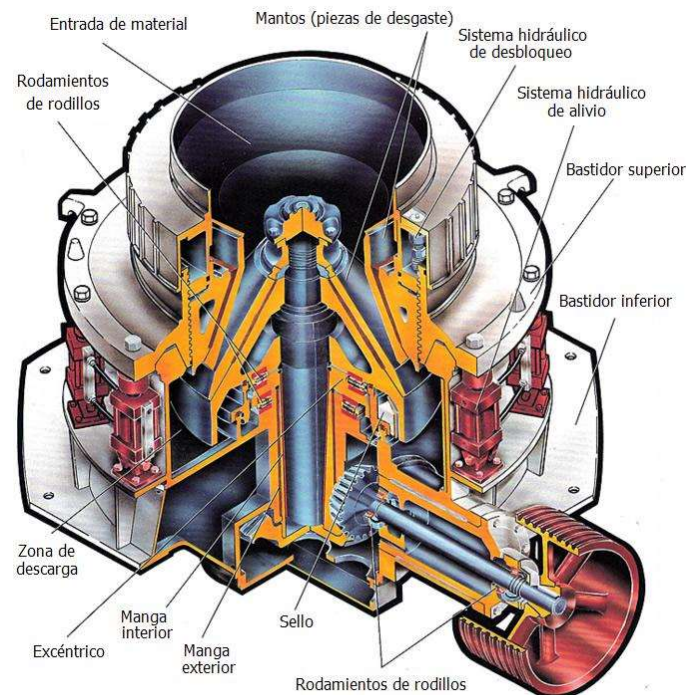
Corte Trituradora giratoria de eje vertical y apoyo inferior
